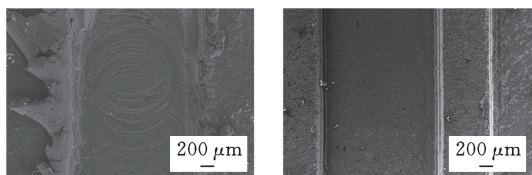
电解加工后工件在不同机械加工深度下的表面形貌
